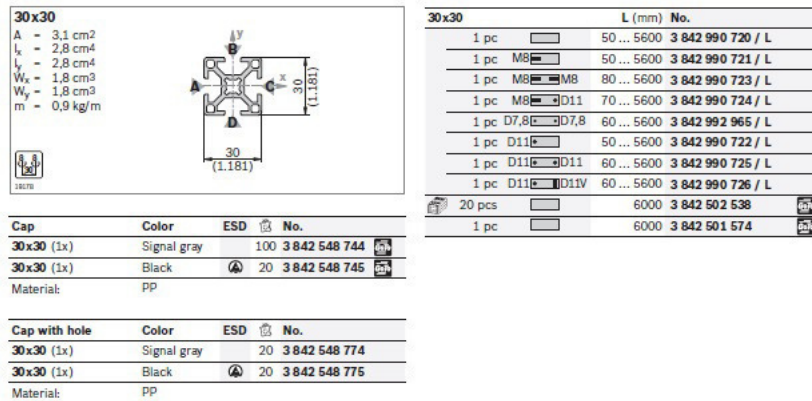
Características da secção transversal do Perfil Bosch 30x30 [23]
